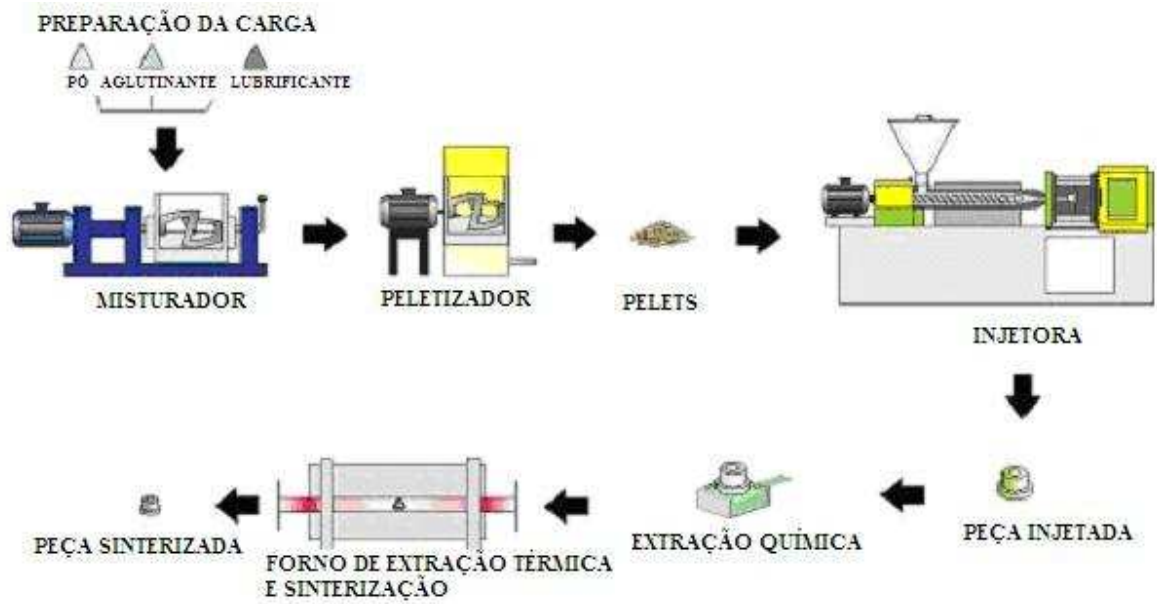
Esquema do processo de moldagem de pós metálicos por injeção.
